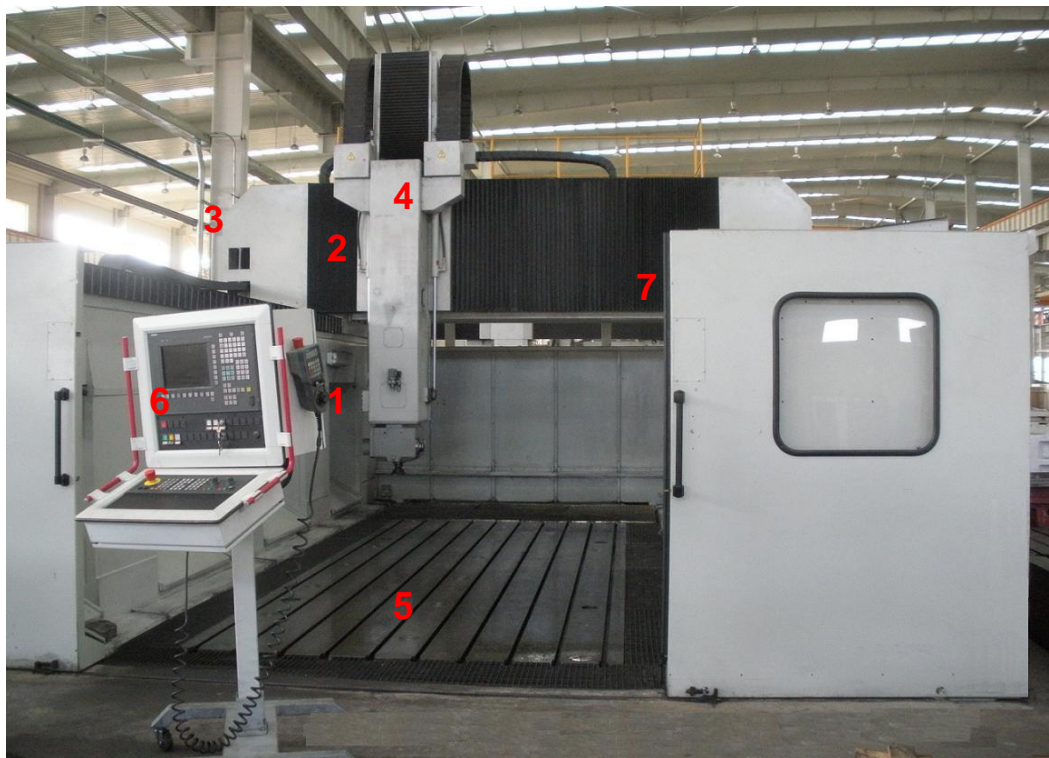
Опытный образец станка ОЦП-3000 на участке сборки завода-изготовителя (ЗАО «Станкотех», г. Коломна)
